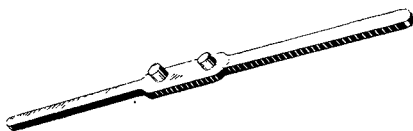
Ключ специальный 47001-1-006МД к пробке дет. 237-24-6 планетарный механизм поворота
